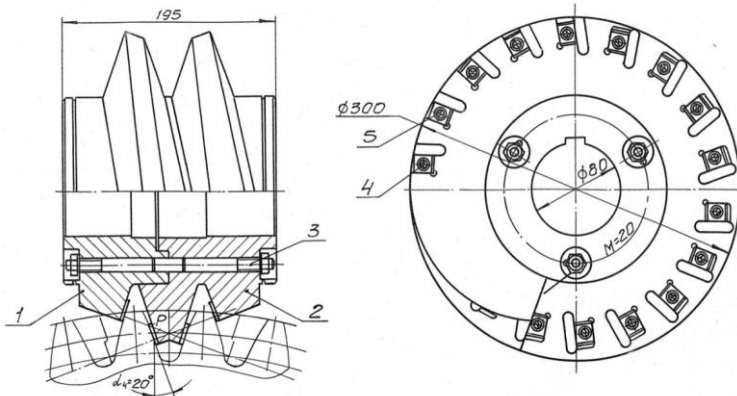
Схема зубофрезерування двухвітковою збірною фрезой
